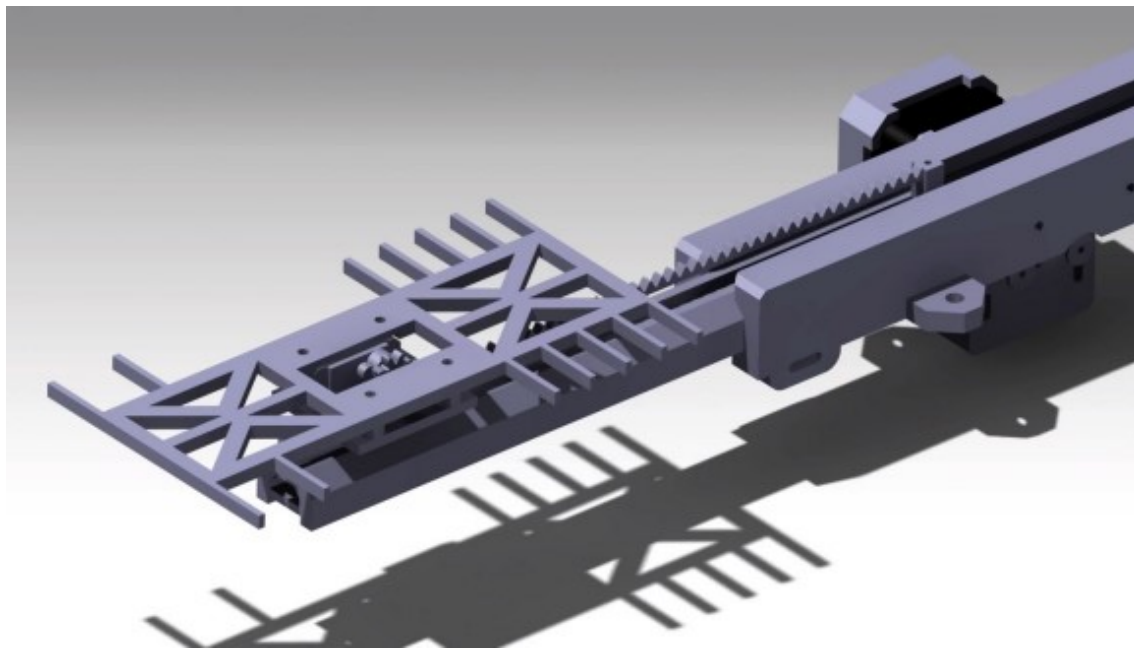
Princip předávání automobilu základacím mechanismem [3]
